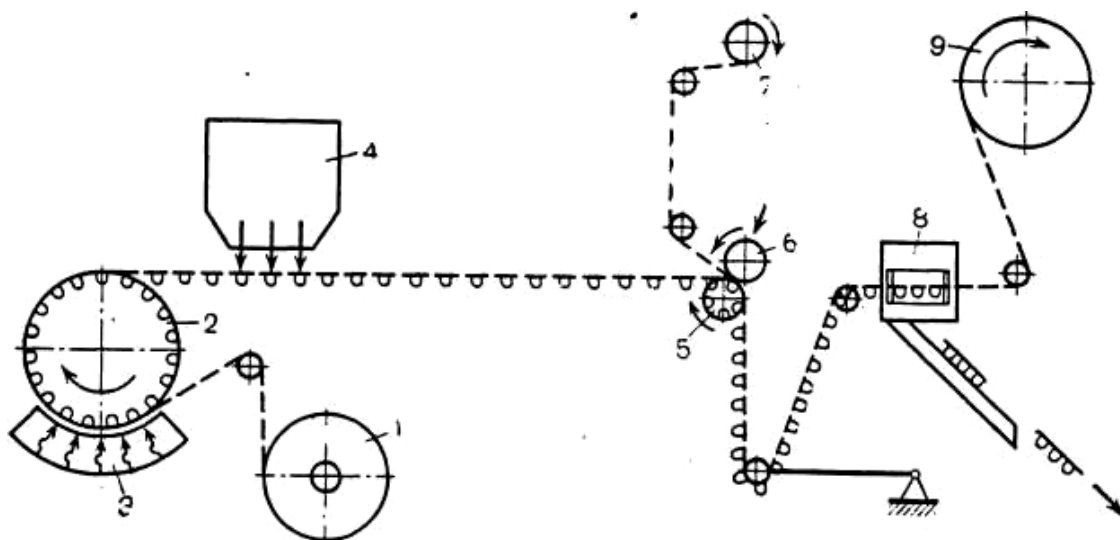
Схема автомату безупинного формування блістерів. 1- рулон з плівкою; 2- формуючий барабан; 3- нагнітальний елемент; 4- бункер; 5,6- нагрівальні валки; 7- рулон з фольгою; 8- вузол штампування та виробки; 9- рулон залишків упаковки (відходи); 10- готова упаковка; 11- натяжний пристій.
